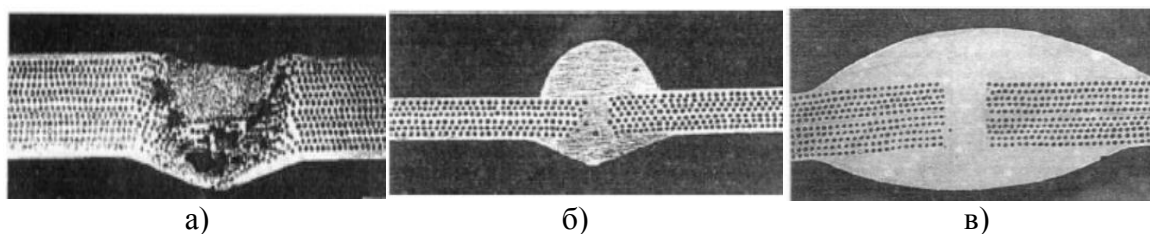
Структура сварных швов сплава 1330/V
